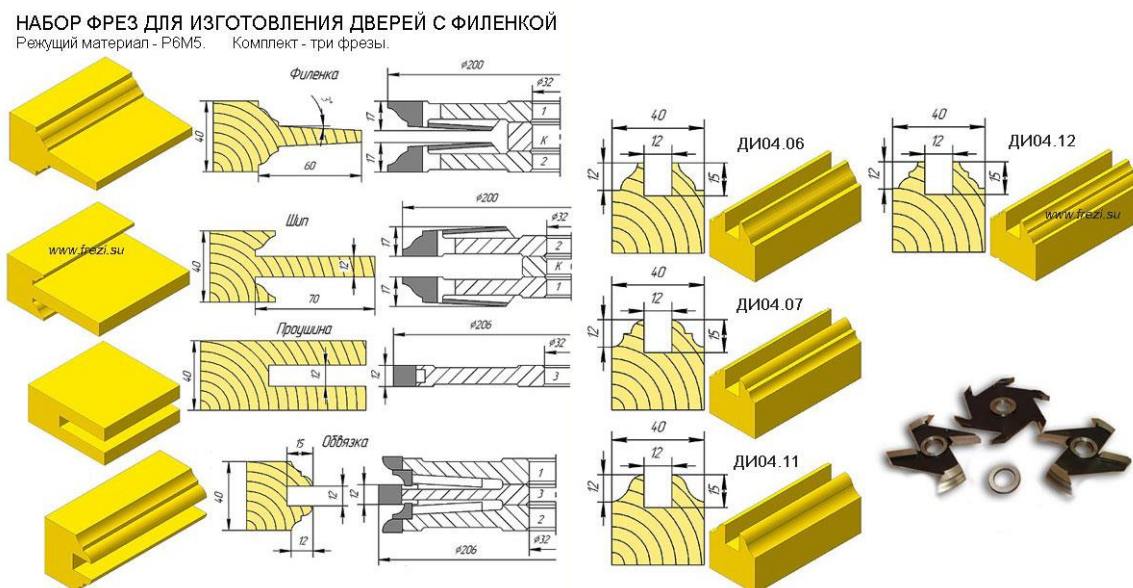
Набор фрез для изготовления дверей с филенкой
